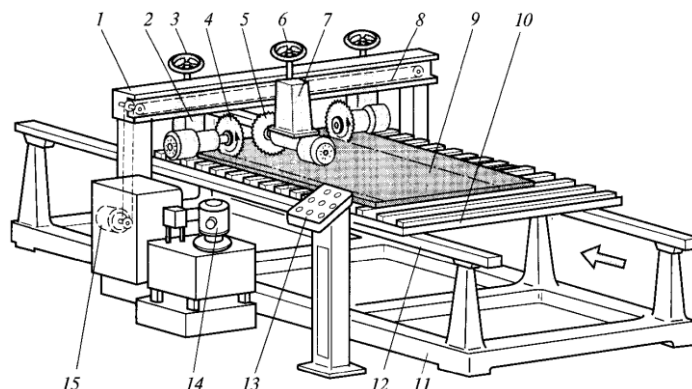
Трипилковий форматно-обрізний верстат: 1 – траверса; 2, 7 – супорти; 3, 6 – маховички; 4 – пилка поздовжнього різання; 5 – пилка поперечного різання; 8 – ланцюг; 9 – розпилюваний матеріал; 10 – каретка; 11 – станина; 12 – напрямна; 13 – пульт керування; 14 – гідростанція; 15 – гідропривід поперечного супорта
